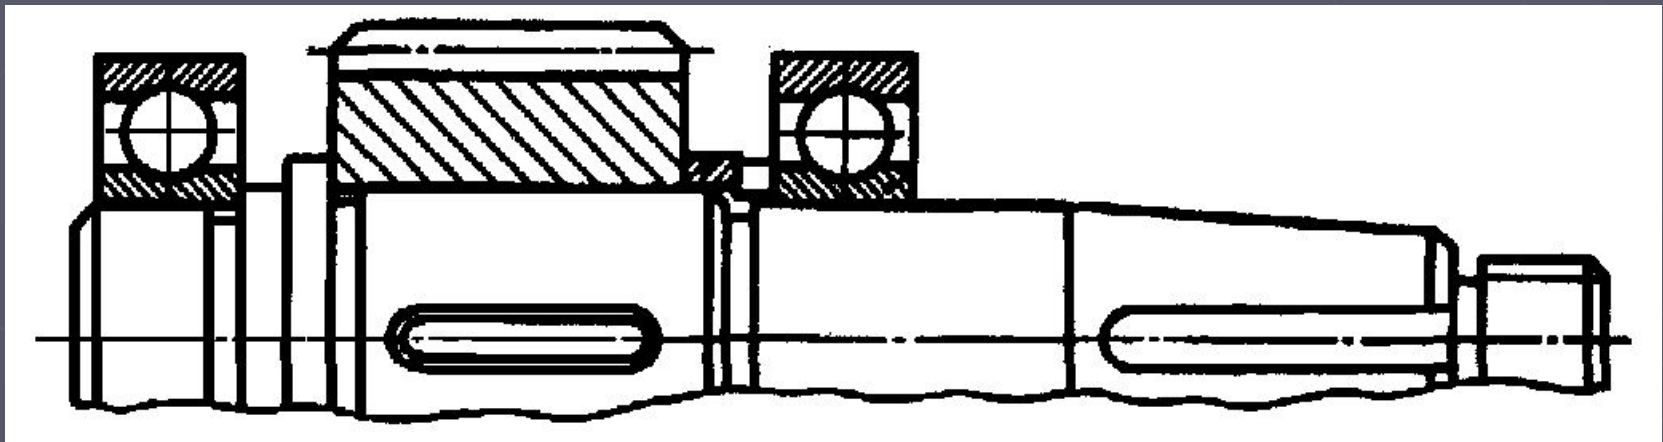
Вал цилиндрической передачи в сборе с шестерней и подшипниками качения.
